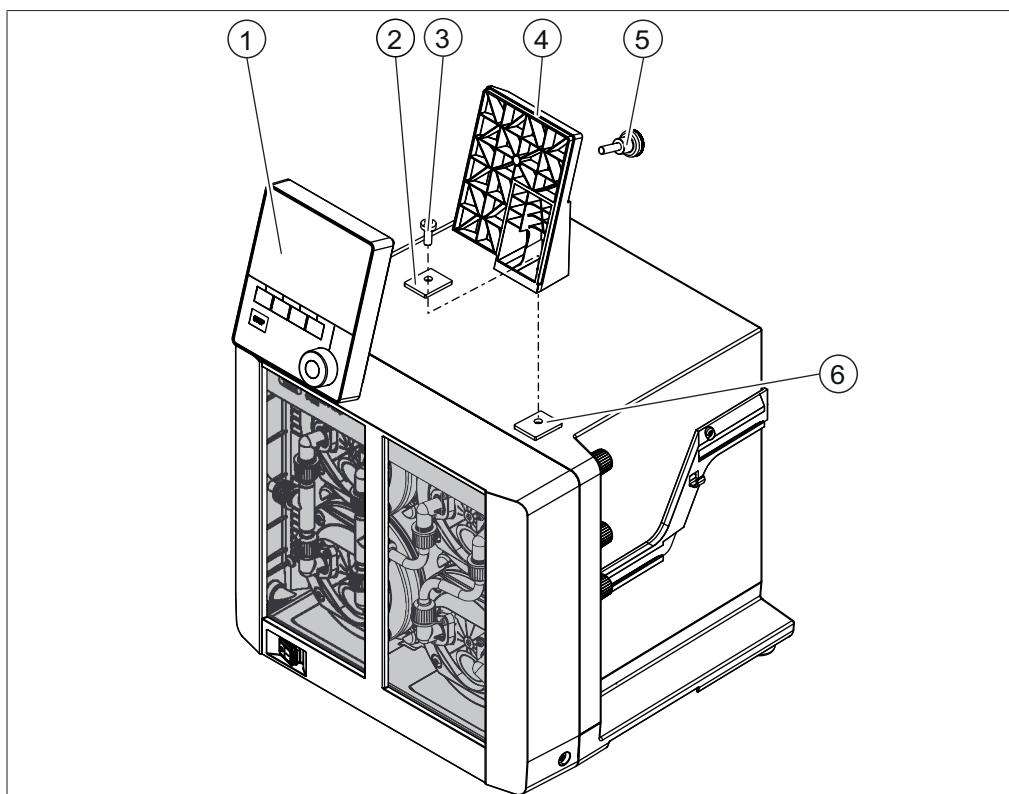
Supporto per il montaggio dell'interfaccia I-300
